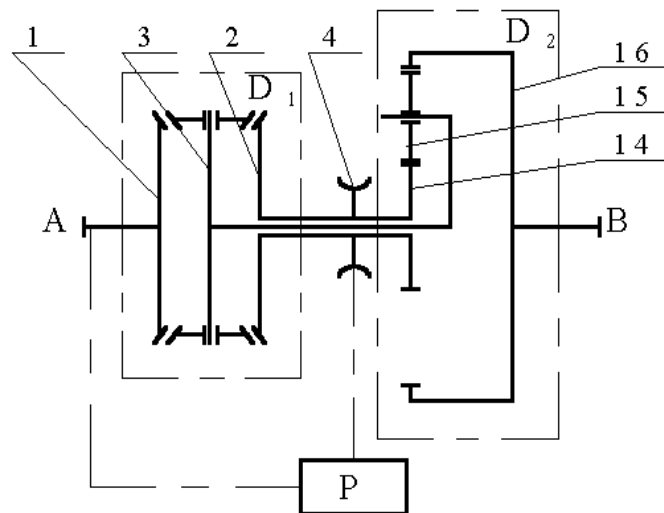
Кинематическая схема передачи с двумя дифференциалами D1 и D2
